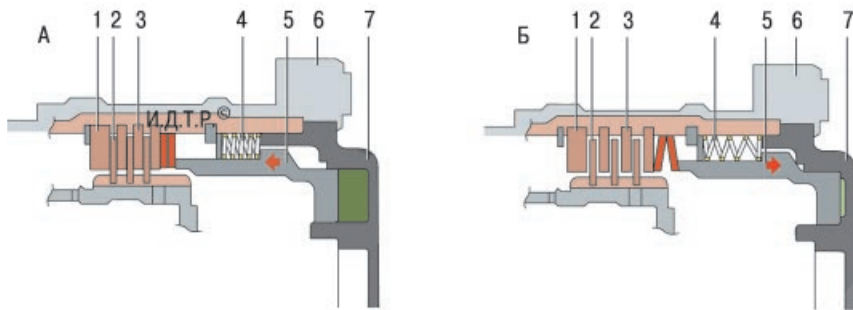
Схема работы дискового тормоза: А – тормоза включены; Б – тормоза выключены; 1 – упорный диск; 2 – фрикционные тормозные диски с накладками; 3 – фрикционный диск; 4 – возвратная пружина; 5 – поршень; 6 – картер коробки передач; 7 – крышка картера коробки передач
